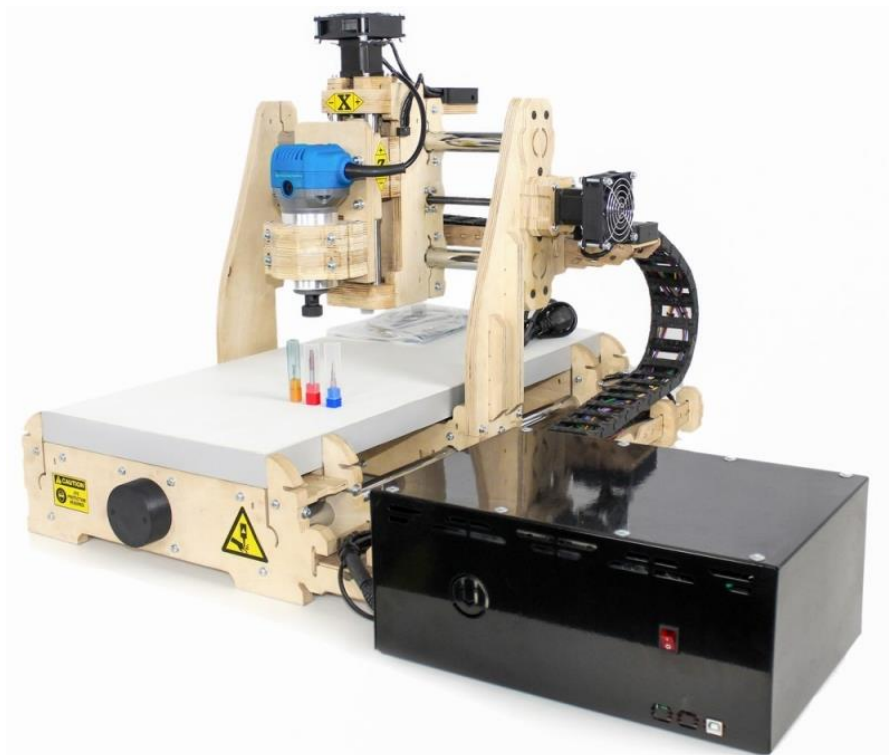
Фрезерно-гравіювальний верстат з ЧПК КРЕЧЕТ 2 [26]
